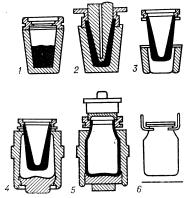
Схема выработки изделий на прессовыдувной машине: 1 — приём капли; 2 — выпрессование пульки в черновой форме; 3, 4 — передача пульки из черновой формы в чистовую; 5 — выдувание изделия в чистовой форме; 6 — отставление готового изделия на конвейер.
